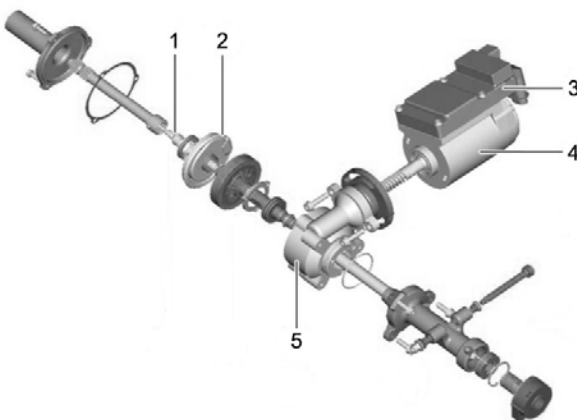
Elektrische Unterstützung an der Lenksäule [3.8]. 1 Torsionsstab, 2 Drehmomentsensor, 3 Steuergerät, 4 Stellmotor, 5 Schneckengetriebe
